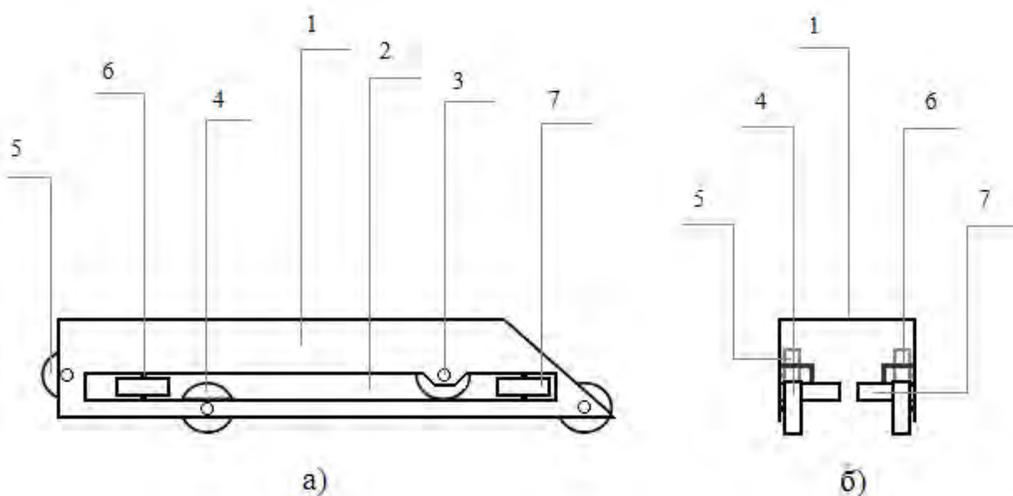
Подвижная платформа: а) вид слева; б) вид спереди.
